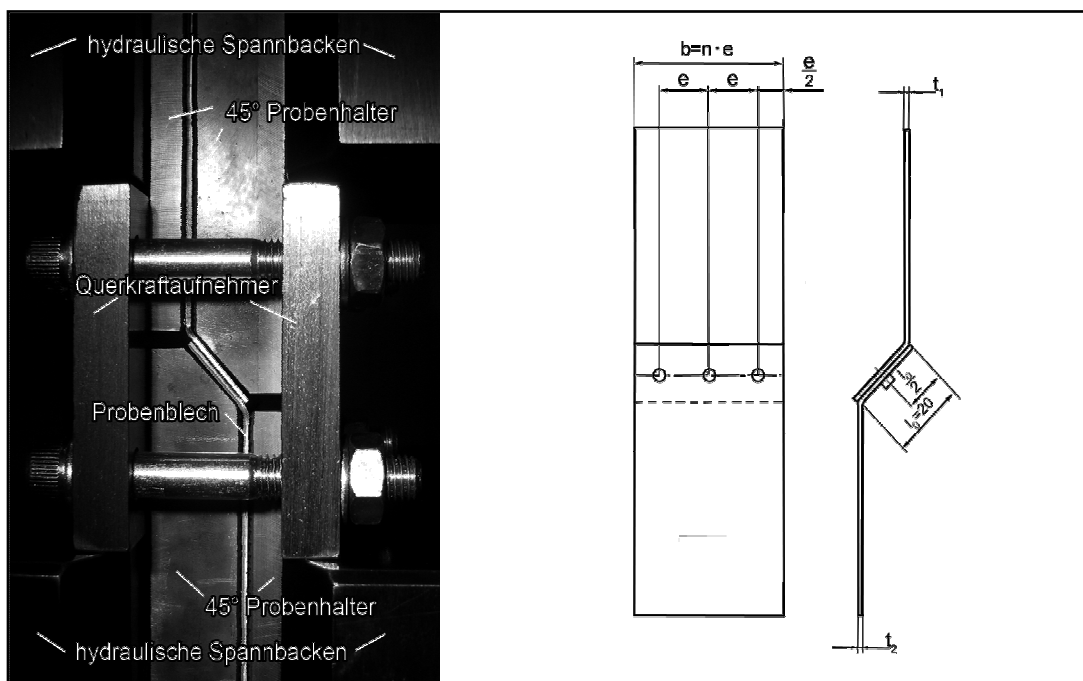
links: 45°-Probenhalter/Spannbacken mit Probenblech und Querkraftaufnehmer im eingebauten Zustand; rechts: Probengeometrie 45°-Schrägzugprobe
